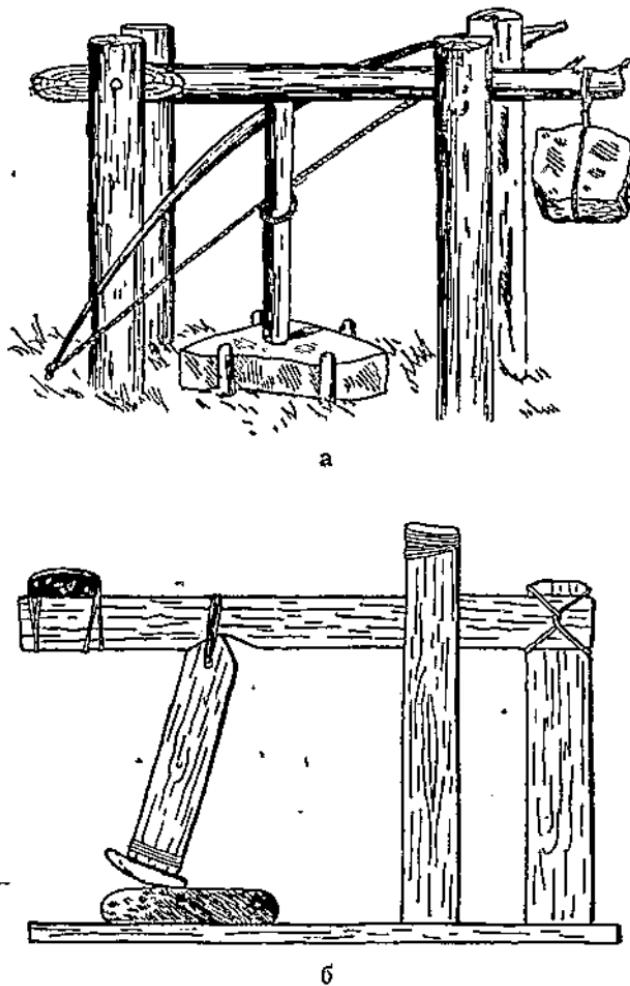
Шлифовальный станок: а—сверление камня; б—шлифование поверхности камня.
